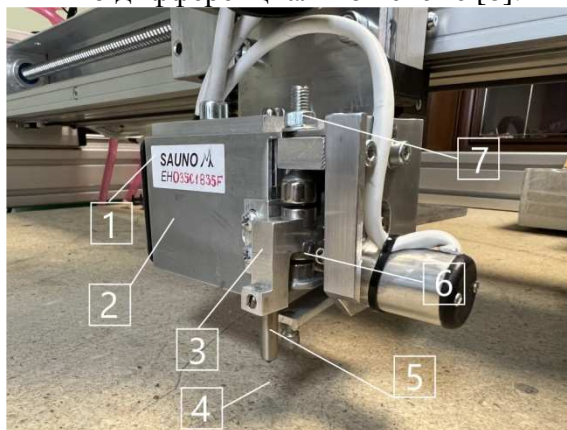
Фото инструментальной головки: 1 – корпус ИГ; 2 – ударный ШД (в корпусе); 3 – рычаг; 4 – картинная плоскость заготовки; 5 – инструмент (алмазная игла); 6 – дифференциальный магнитный подвес; 7 – микрометрический винт.
